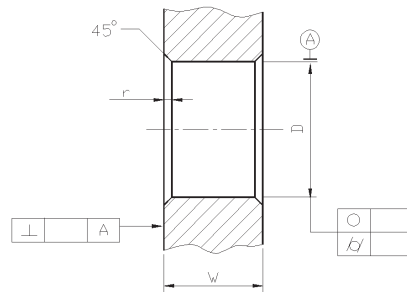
外圈带安装槽类型关节轴承轴承座孔的形位公差
